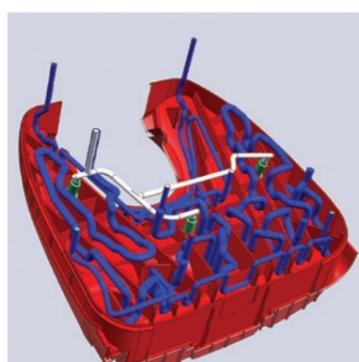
LaserCUSING® Werkzeugeinsatz für Staubsaugerdeckel in patentierter Hybridbauweise mit konturnahen Kühlkanälen.
